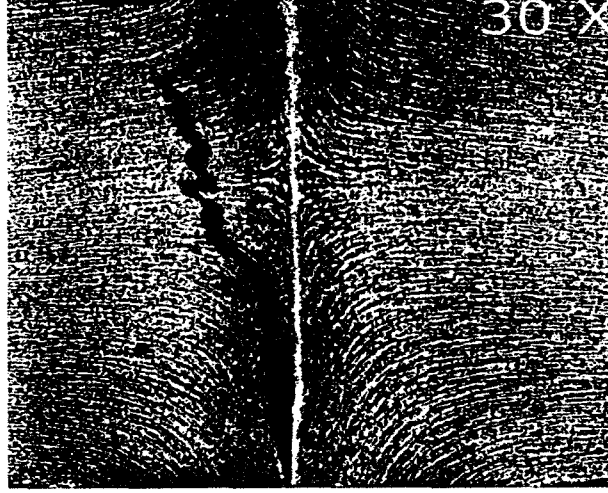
Kaynak dikiş bölgesinde sıkışmış gaz boşlukları
